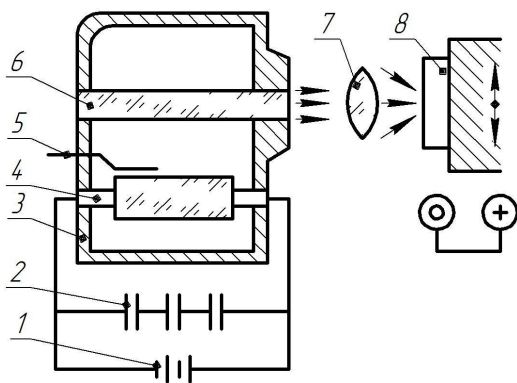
ОКГ: 1 – джерело струму; 2 – батарея конденсаторів; 3 – корпус; 4 – імпульсна лампа; 5 – пусковий пристрій; 6 – рубін; 7 – лінзи; 8 – заготовка
